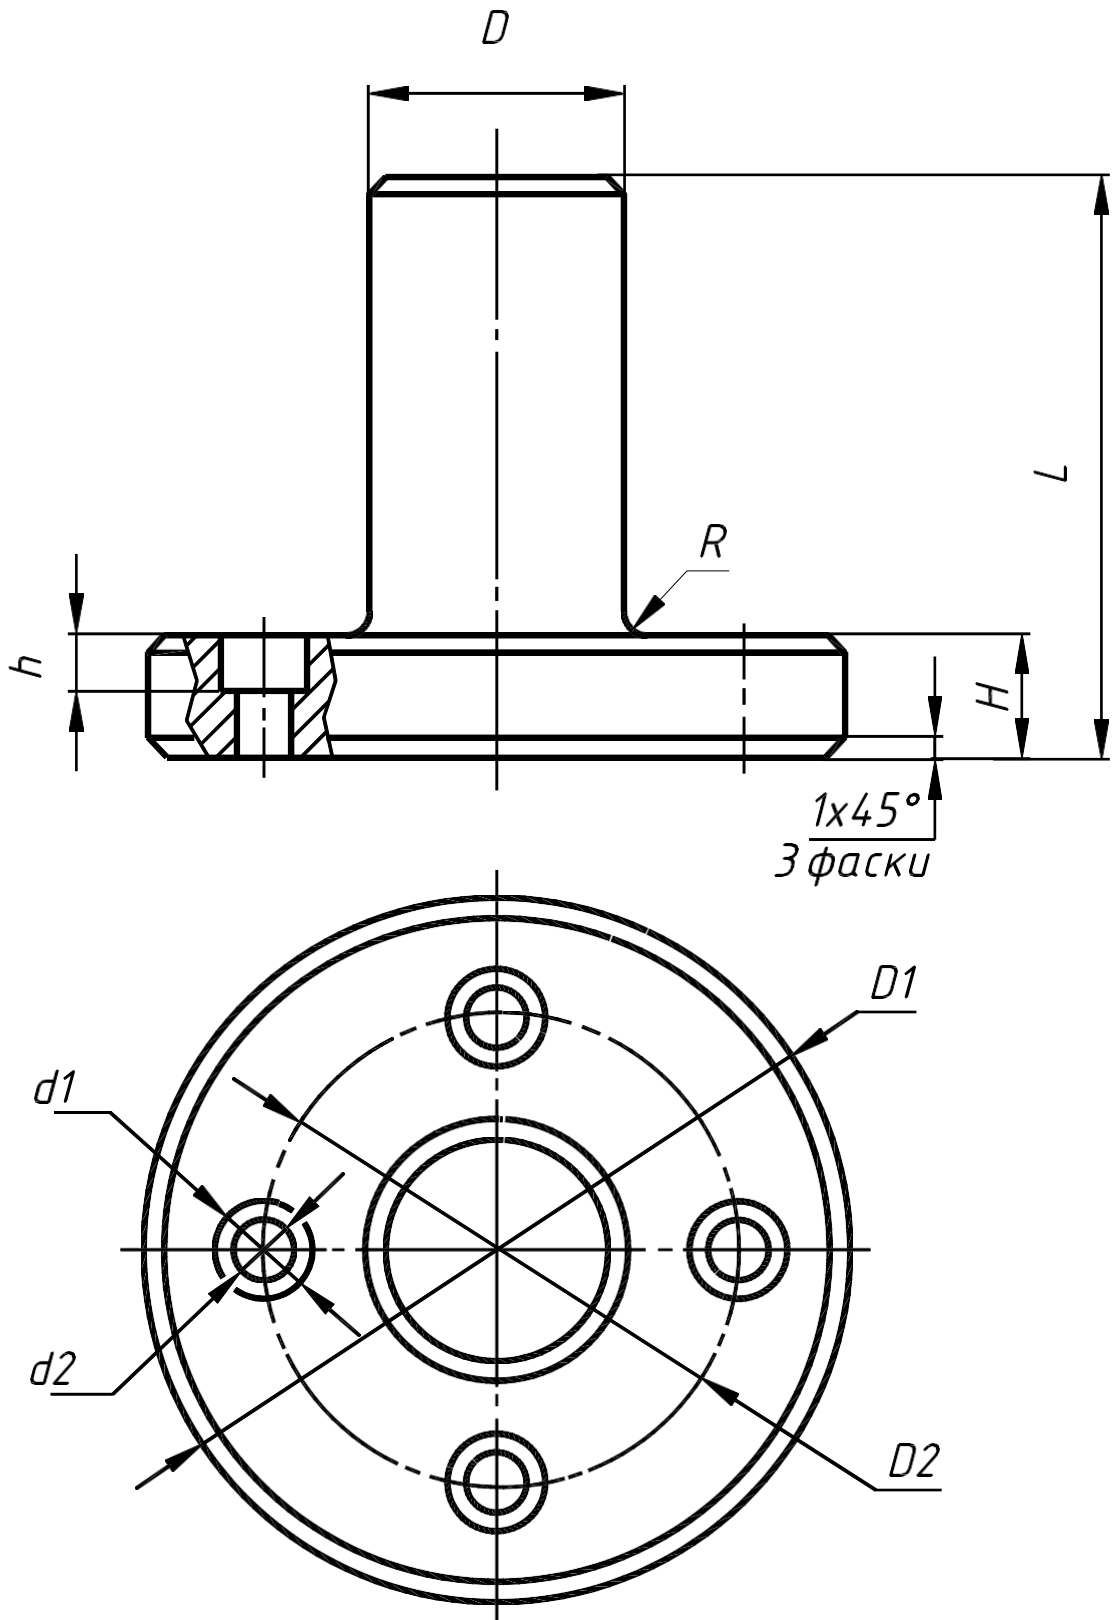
Чертеж с параметрами хвостовика к верхней плите блока штампа
